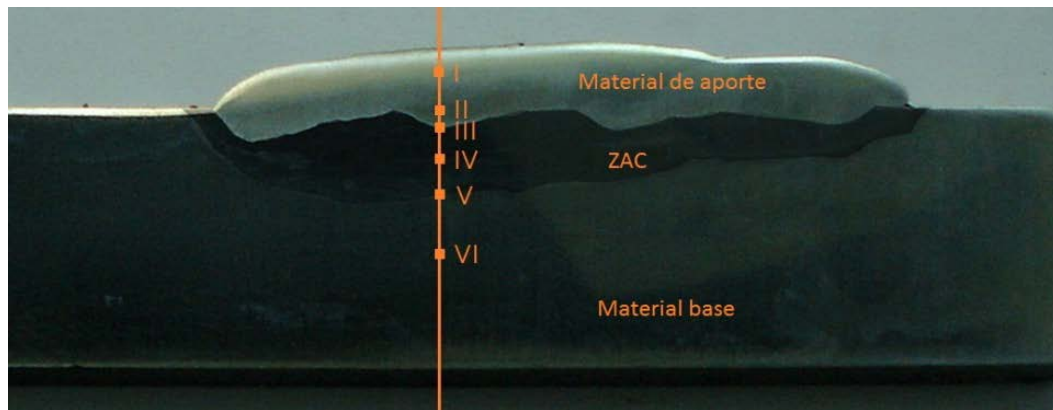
Zonas de microindentación en las probetas de soldadura.
